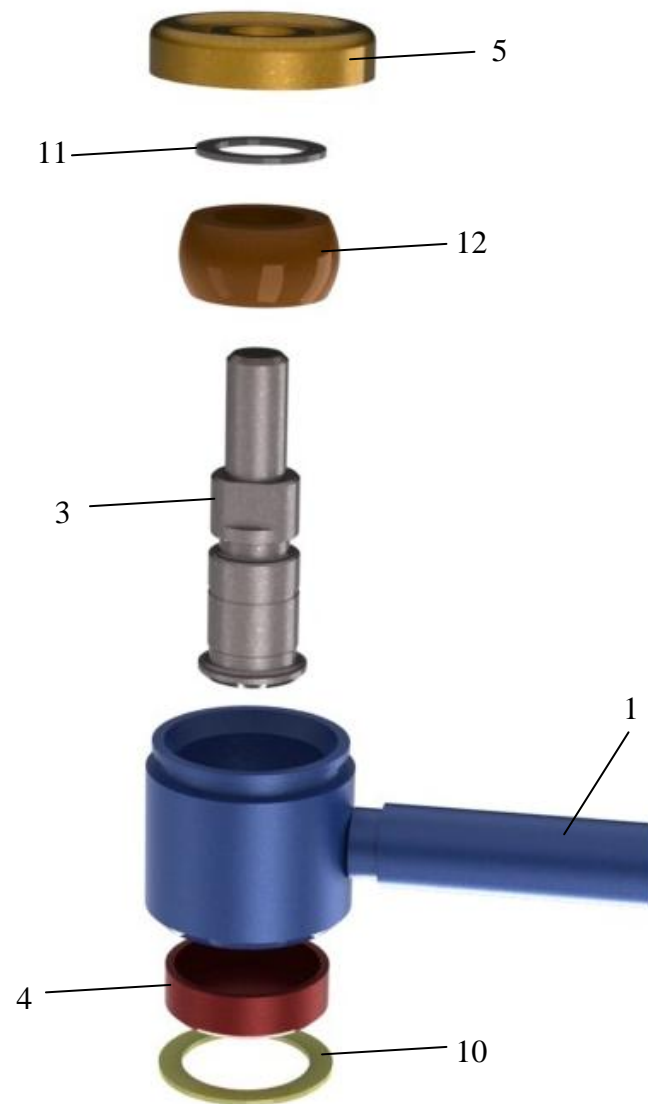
Шарнир верхний АКСМ 321-131601.600
